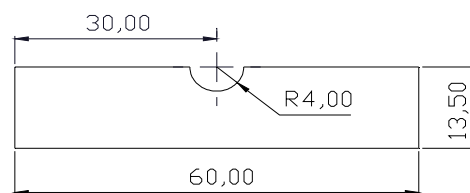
Ranura en cupón de soldadura de 60x60x13.5 mm.
